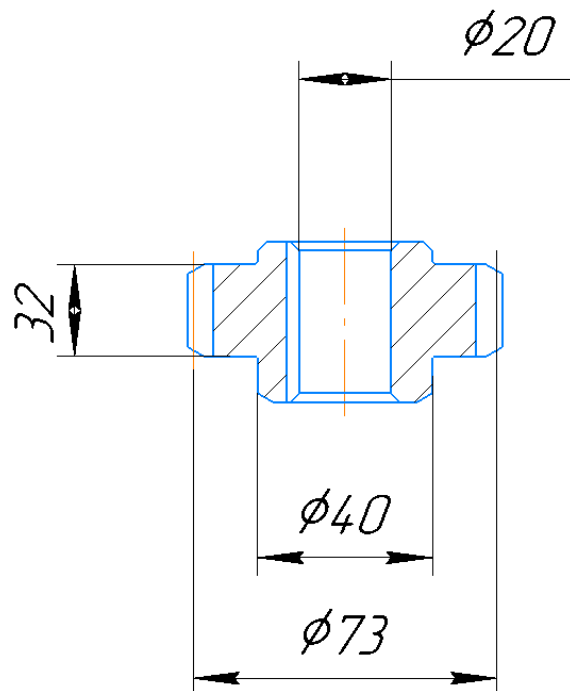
Схема тихохідного зубчатого колеса Н₂
